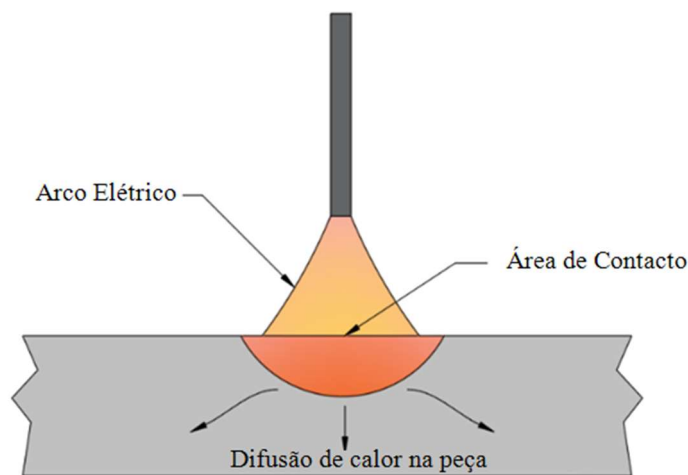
Ilustração esquemática do fluxo geral de calor na soldadura por fusão. Adaptado de [7]
